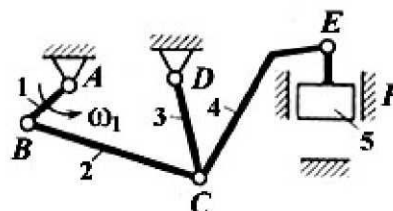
Механизм ковочно-штамповочного прессы
